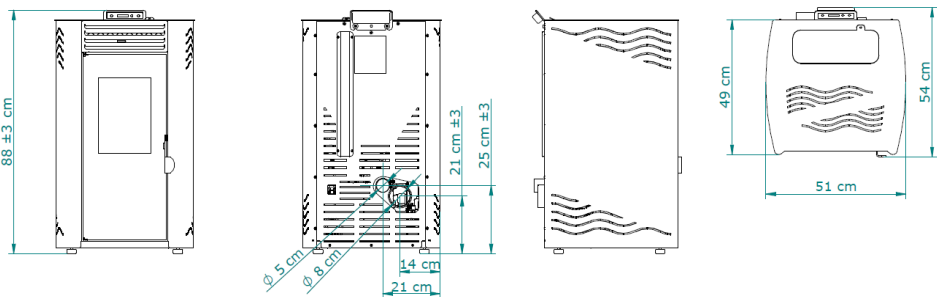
B – Dimensiones de la estufa de pellets Folk 8 kW
